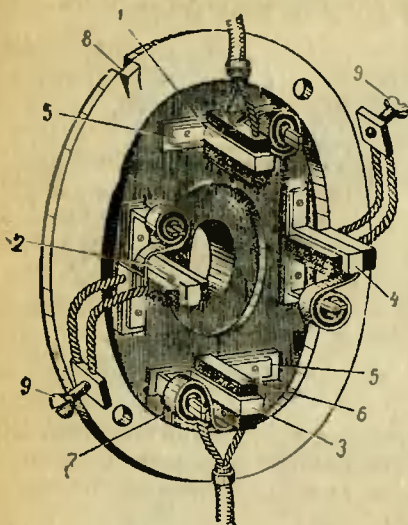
Крышка стартера со щеткодержателями: 1, 2, 3 и 4 — щеткодержатели, 5 — изоляционные пластинки для изоляции щеткодержателей от крышки, 6 — щетки, 7 — нажимные пружины щеток, 8 — установочный выступ, 9 — винты для соединения щеток с массой.
